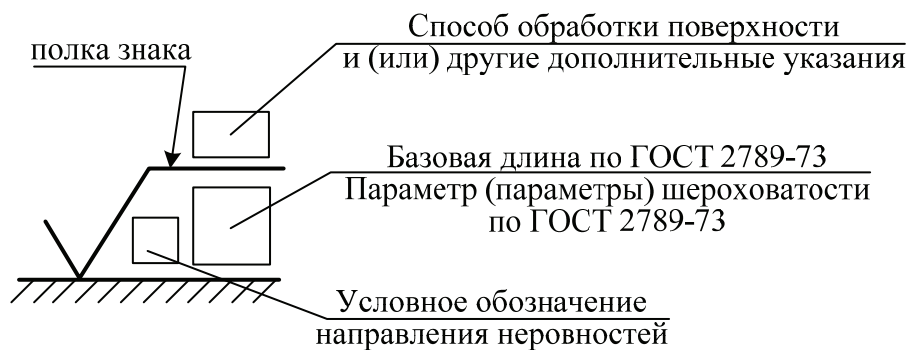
Структура обозначения шероховатости поверхности на чертежах
